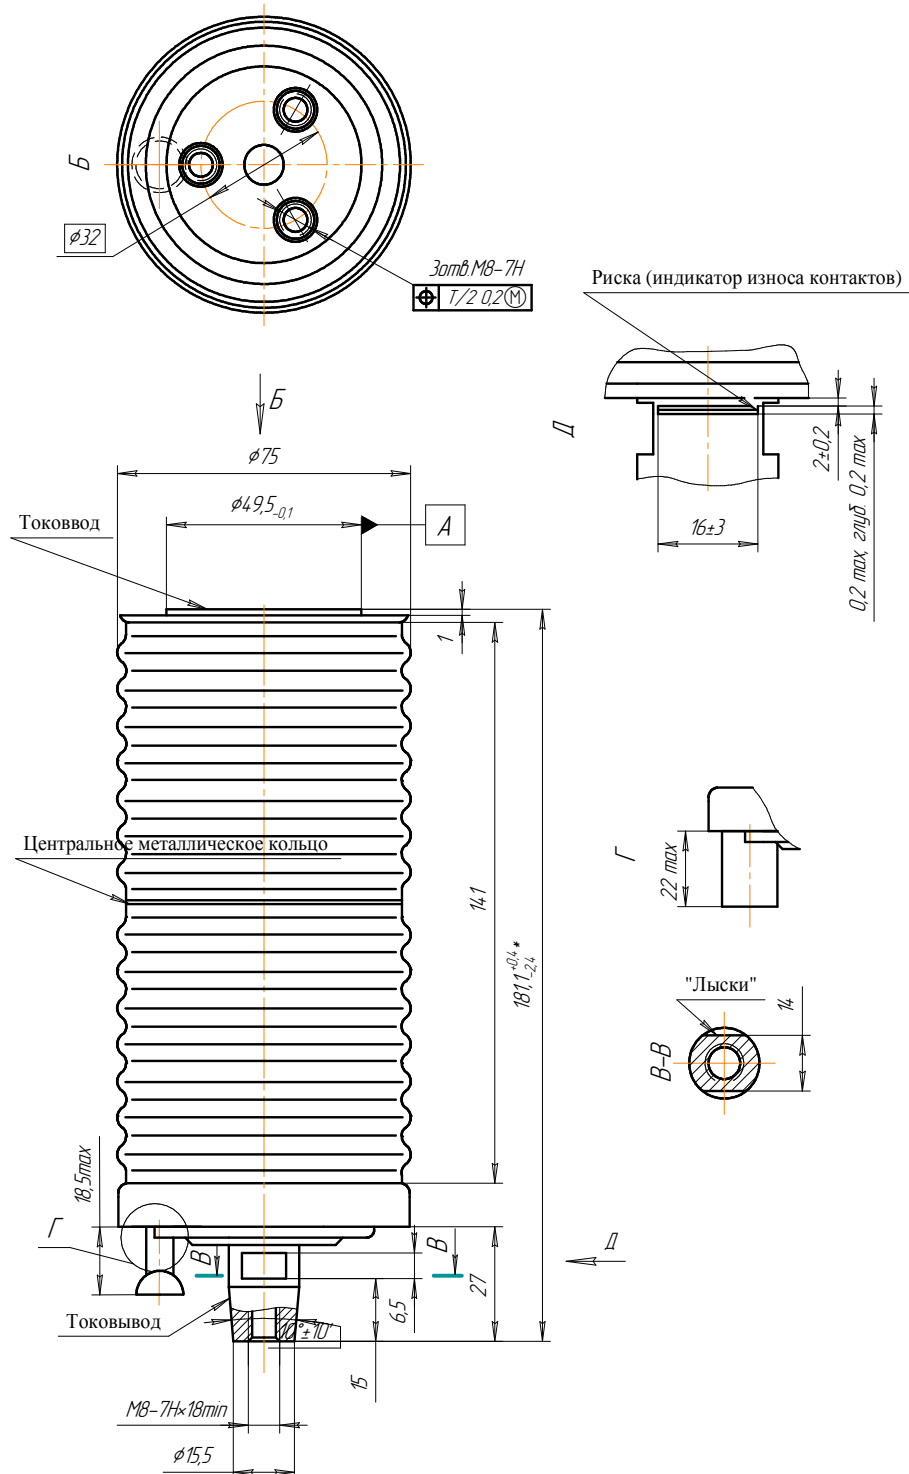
Габаритные, присоединительные и установочные размеры камеры типоразмера КДВЗ-10-5/400 УХЛ2
